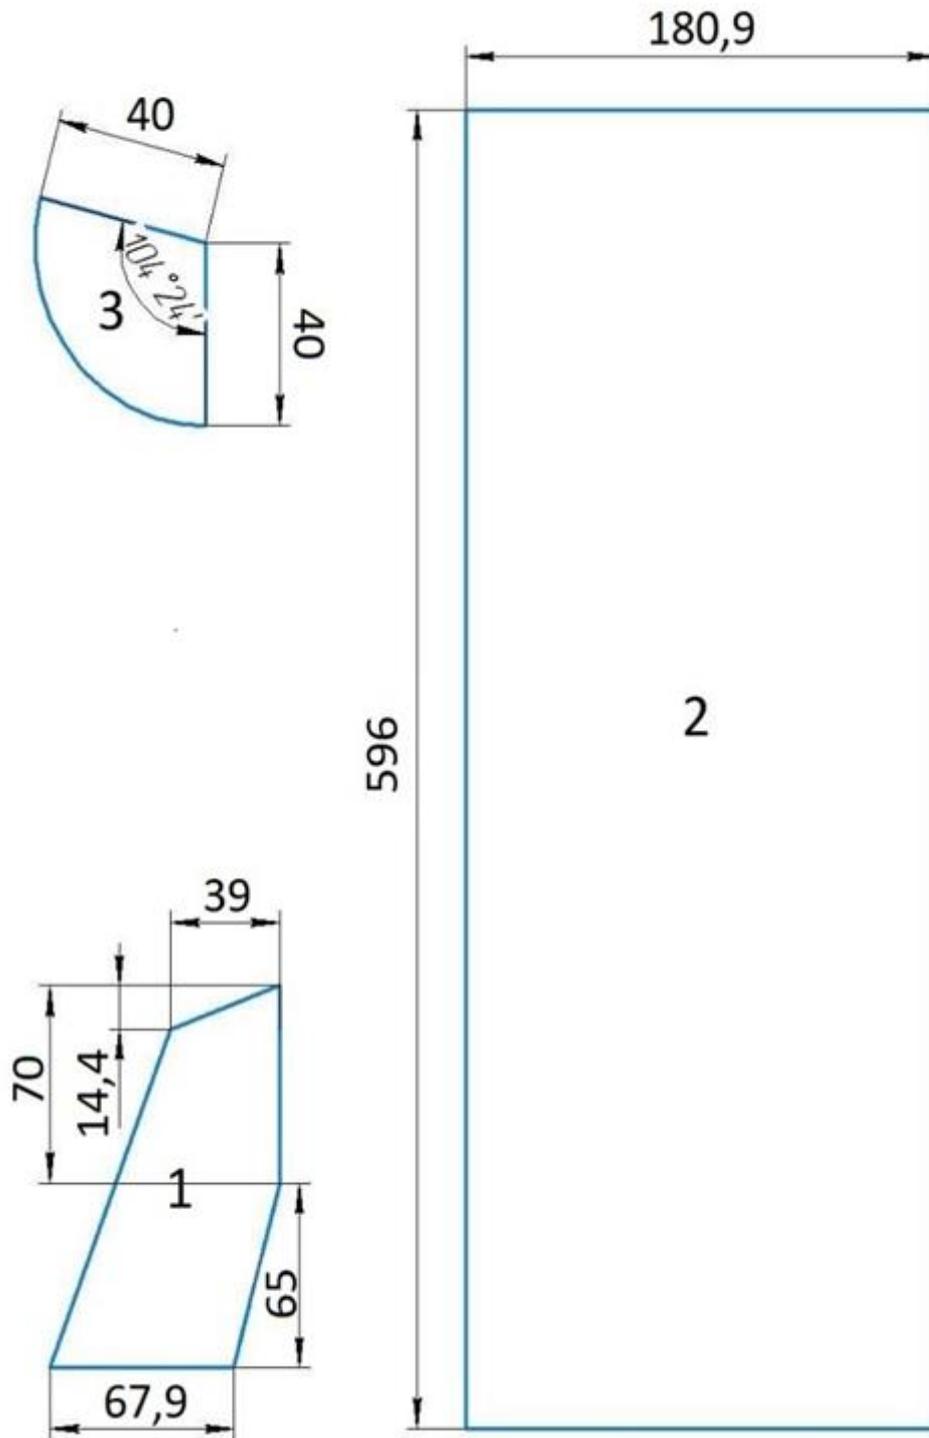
«Чертеж-выкройка», деталей опытного образца:
